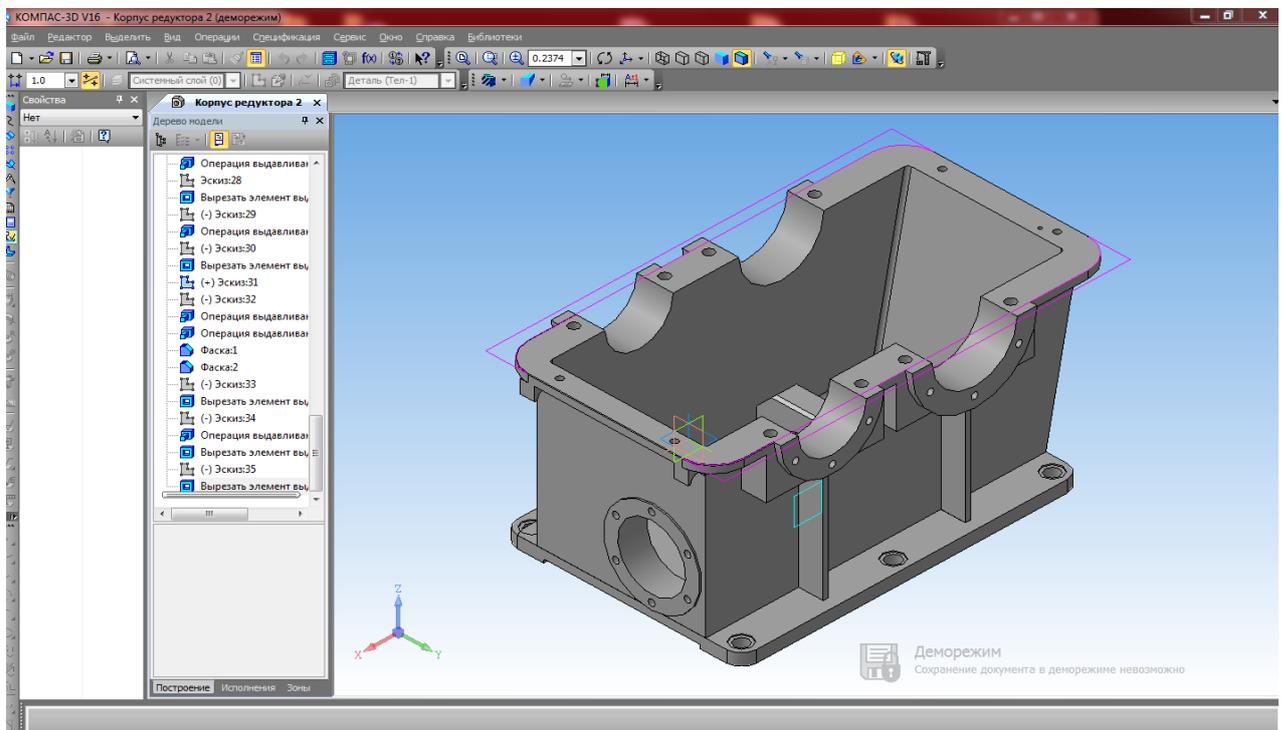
Трёхмерная модель детали «Корпус редуктора»
